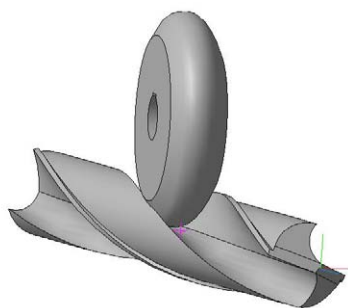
Модели обрабатываемой и инструментальной поверхностей при вышлифовывании стружечной канавки сверла
